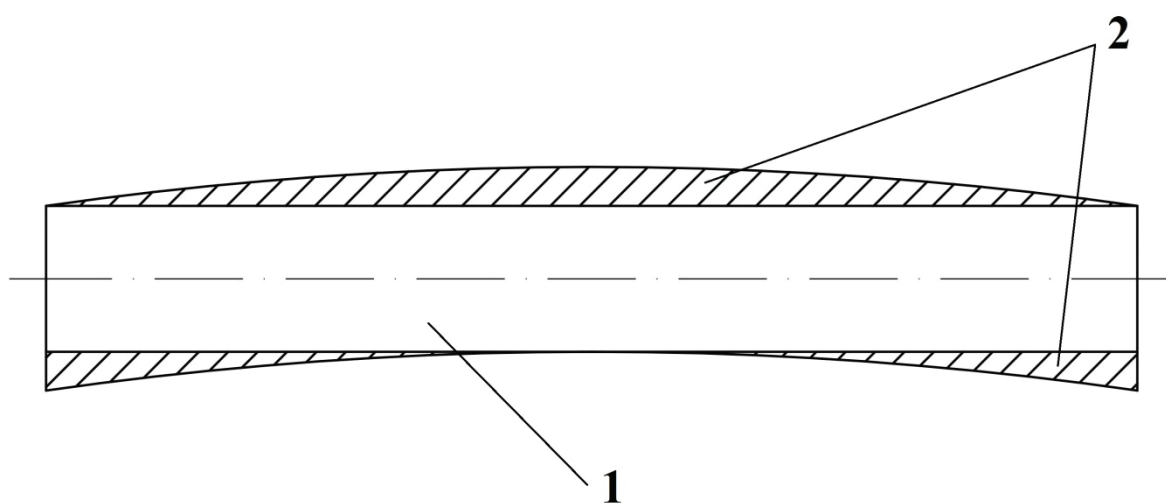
Схема оцилиндровки бревна обладающего кривизной: 1 — получаемый стержень цилиндрической формы; 2 — срезаемый слой
